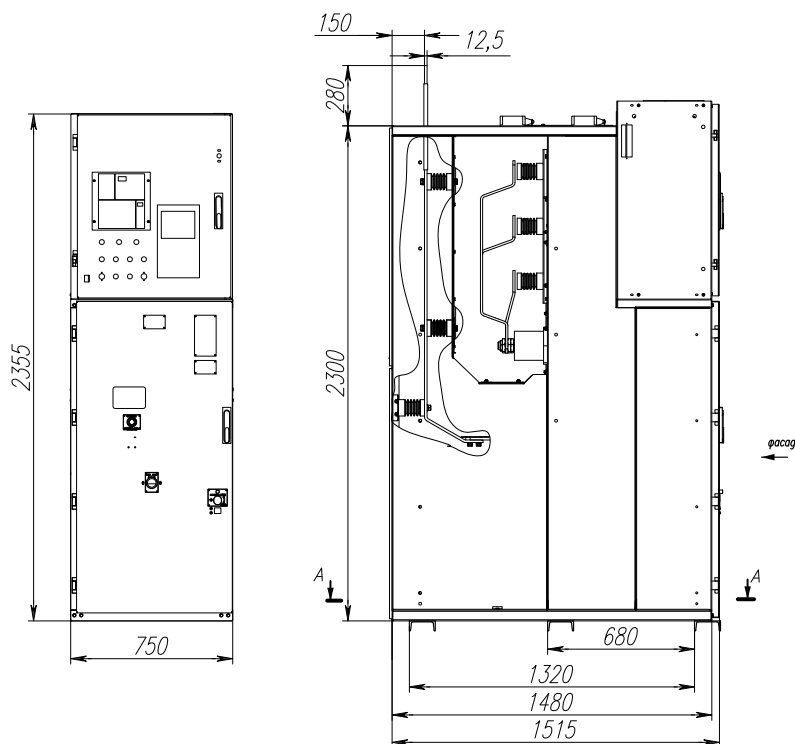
Общий вид и габаритные размеры шкафа шинного ввода на номинальные токи до 1600 А
